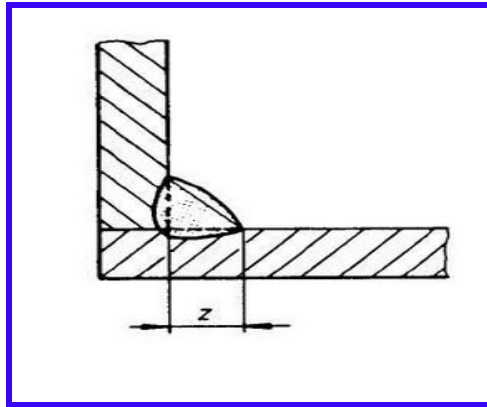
Soldadura. [Fuente: 10]
